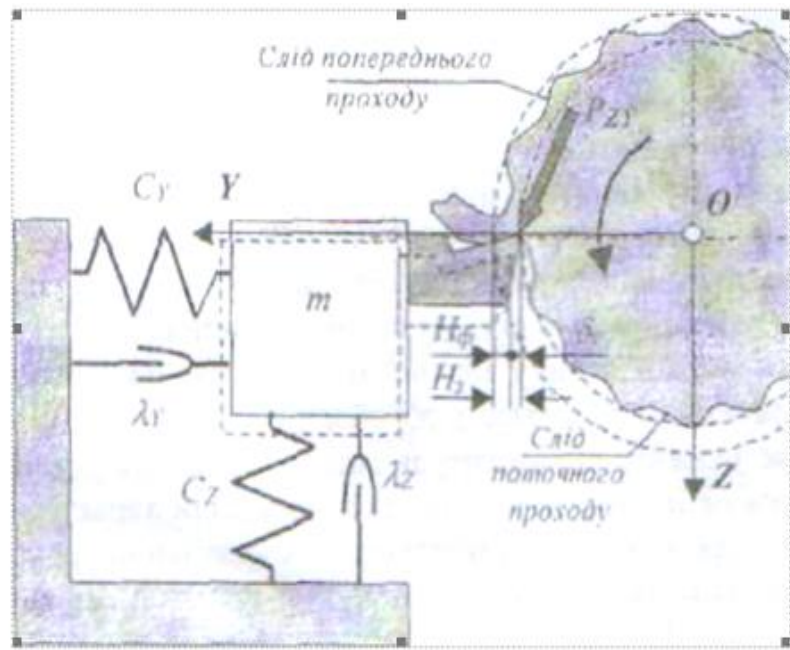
Динамічна схема ТОС токарного верстата
